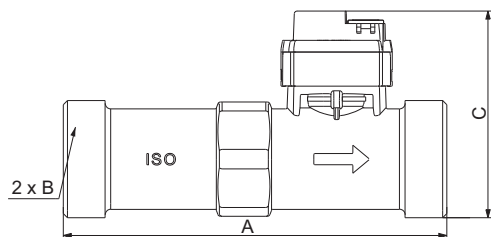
Размеры, VFS QT, 10-200 л/мин, с резьбовыми соединениями
